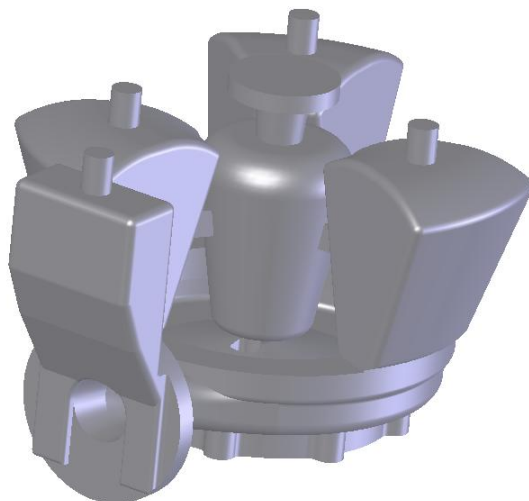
Отливка «Корпус насоса» с литниково-питающей системой
